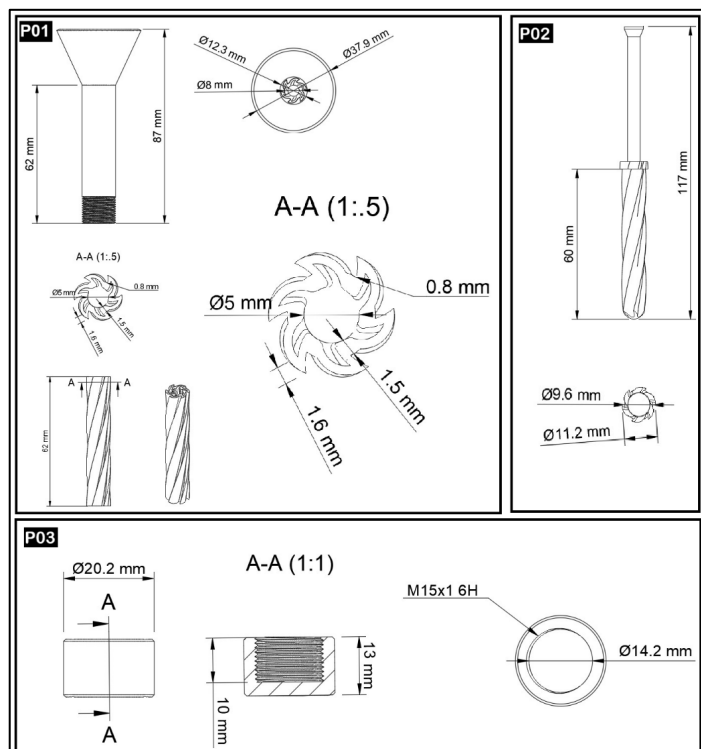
Dimensões das peças do molde projetado. (P01) corpo cilíndrico, (P02) êmbolo extrusor, (P03) tampo/molde para disco.
